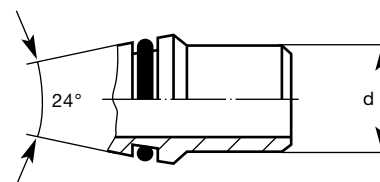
Raccord vissé avec surface d'étanchéité conique à 24° : forme A pour connecteur soudé
